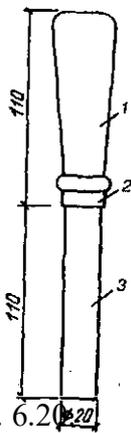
Штыковка для укладки раствора в форму-конус
